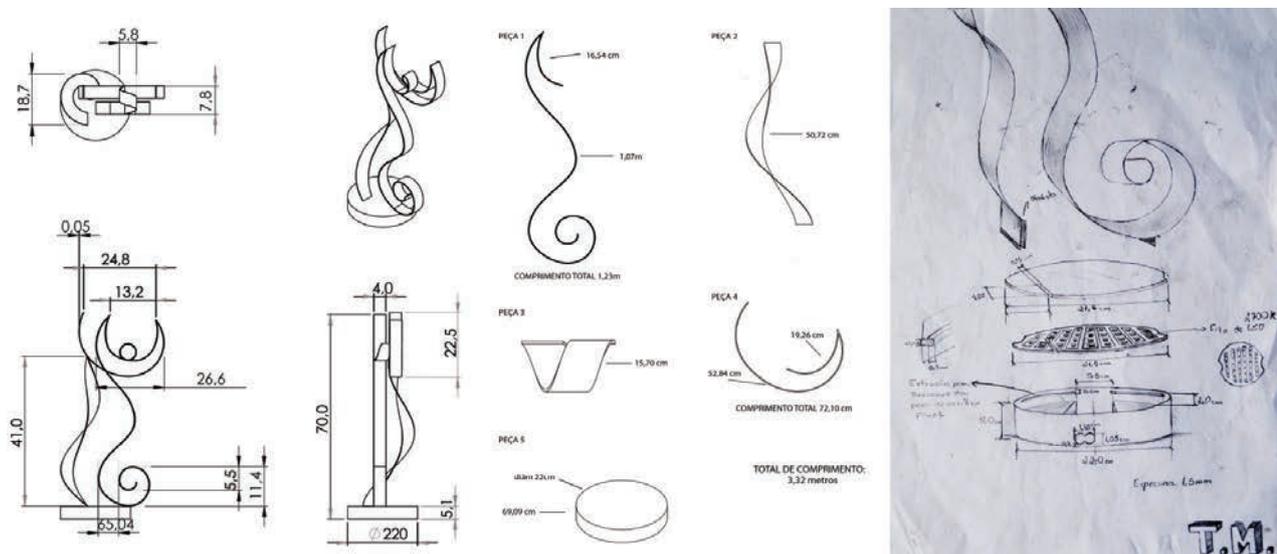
Desenho técnico e esboço da montagem da chapa com LED e seus acessórios.
